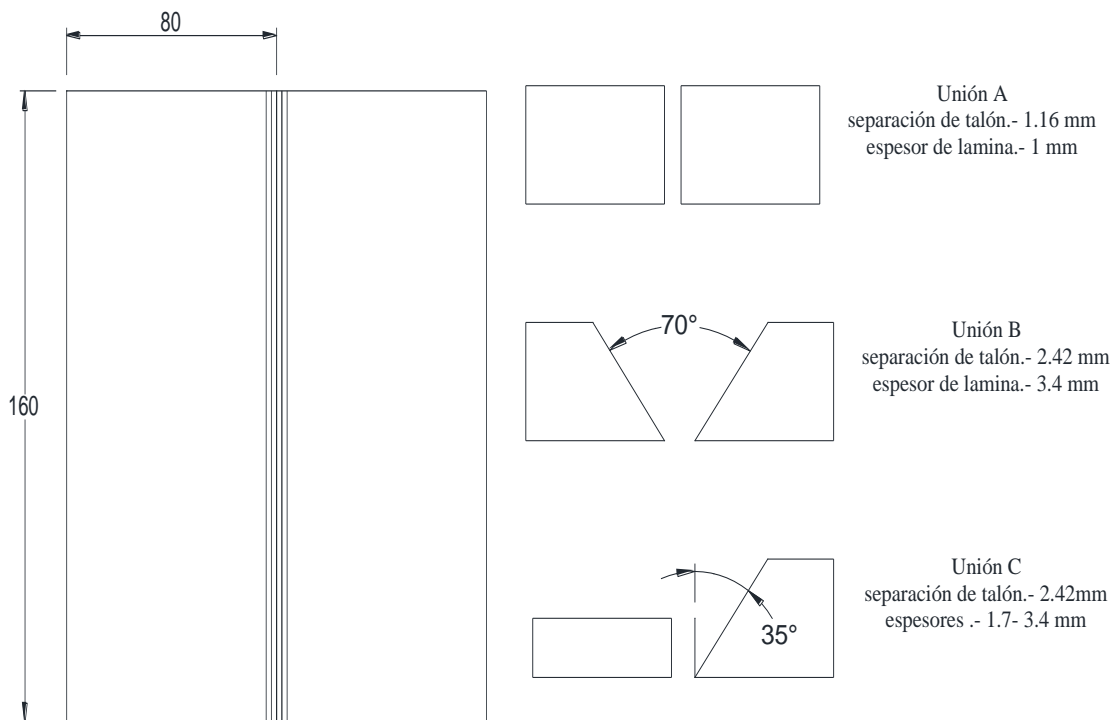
Probetas soldadas de Hastelloy X y diseño de juntas para las uniones A, B y C.
